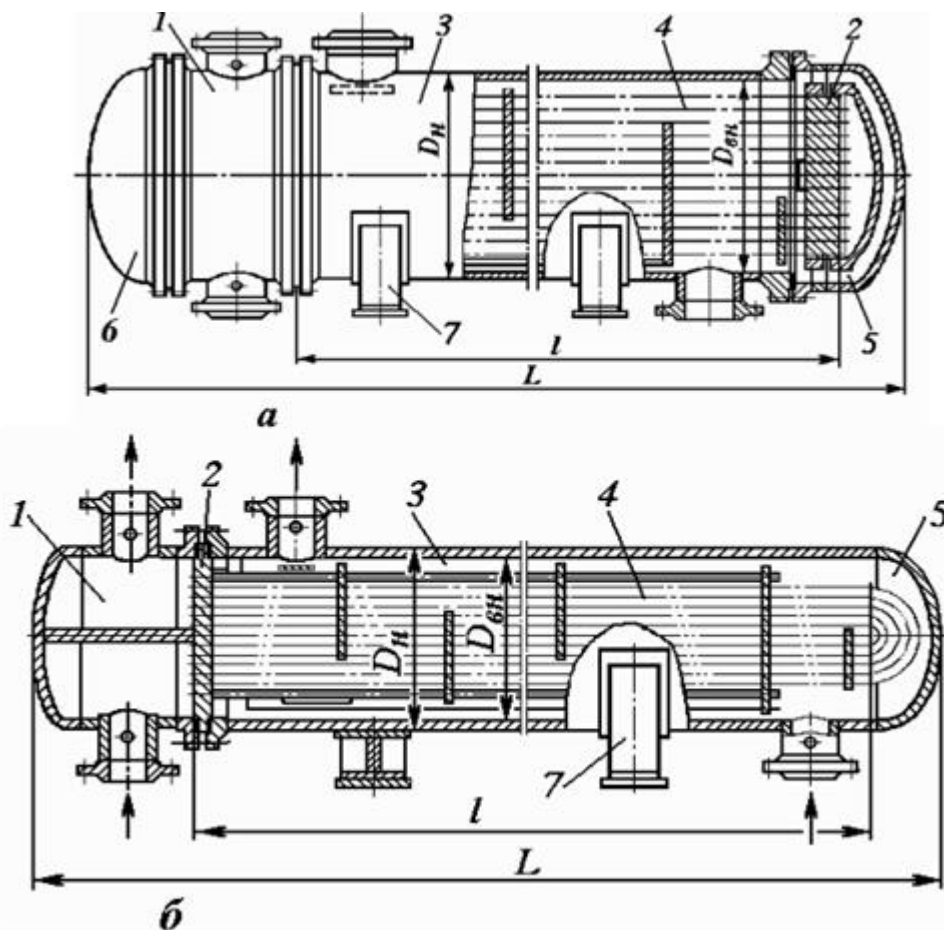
Нежорсткі кожухотрубні теплообмінники: а - з плаваючою головкою (тип ТП); б - з П-подібними трубами (типу ТУ); 1 - роздавальна; 2 - трубна плита; 3 - корпус; 4 - труба; 5 - задня кришка; 6 - передня кришка; 7 - опорний кіготь
